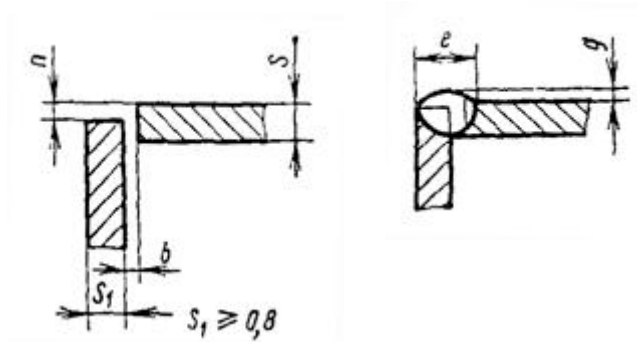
Эскиз сварного соединения У4 ГОСТ 14771-76
